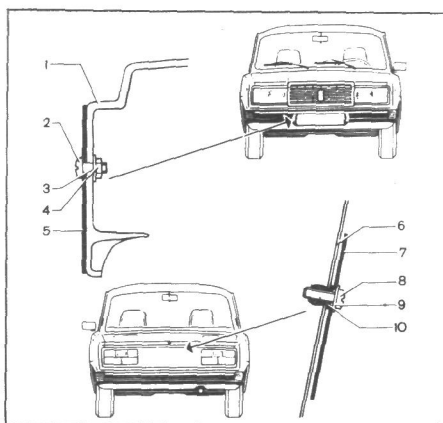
Крепление номерных знаков: 1 — передний бампер; 2 — винт; 3 — шайба; 4 — гайка; 5 — передний номерной знак; 6 — задняя стенка багажника; 7 — задний номерной знак; 8 — самонарезающий винт; 9 — шайба; 10 — пластмассовая втулка
